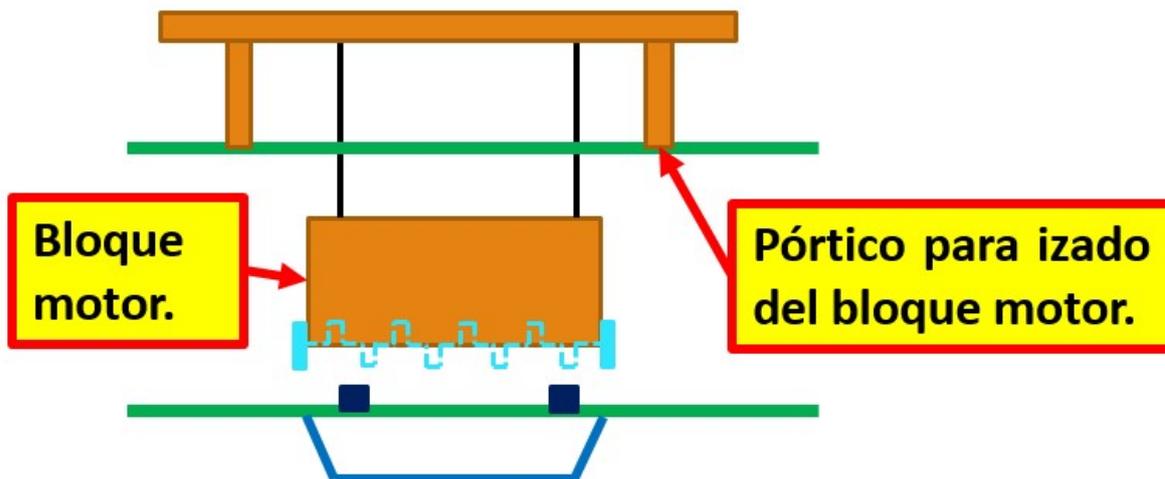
Bloque izado. Fuente: Trabajo de campo.
